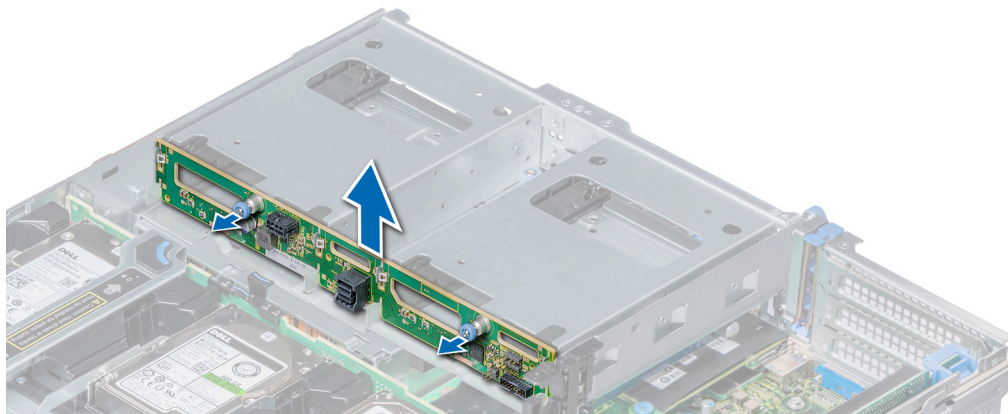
Entfernen der Rückwandplatine des hinteren 3,5-Zoll-Laufwerks
